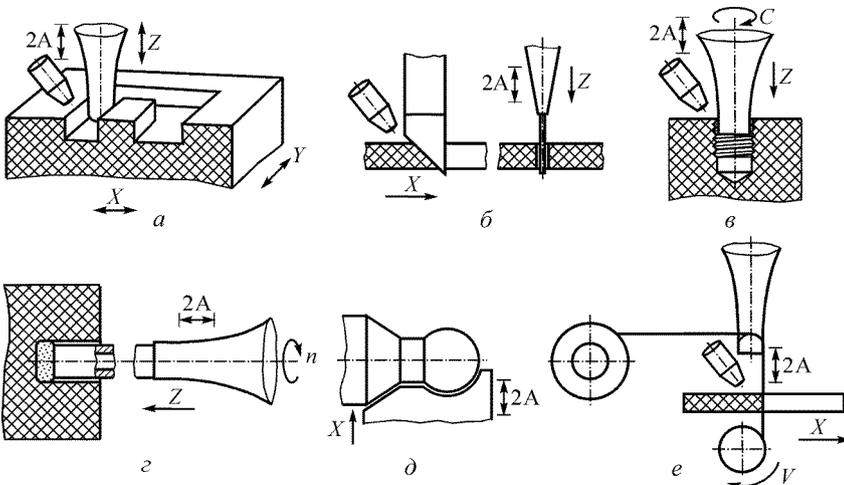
Некоторые операции ультразвуковой обработки: а — фрезерование; б — резка; в — нарезание резьбы; г — прошивка глубокого отверстия; д — точение; е — резка (вырезка) проволочным инструментом
